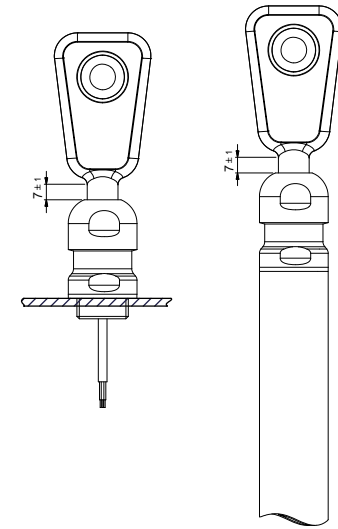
pms-Sensor D12-Adapterschaft mit Sensorverschraubung BF-pms/A1 befestigt am Maschinenteil oder am Edelschrauhrohr D26,8 mit Innengewinde M20x1,5
